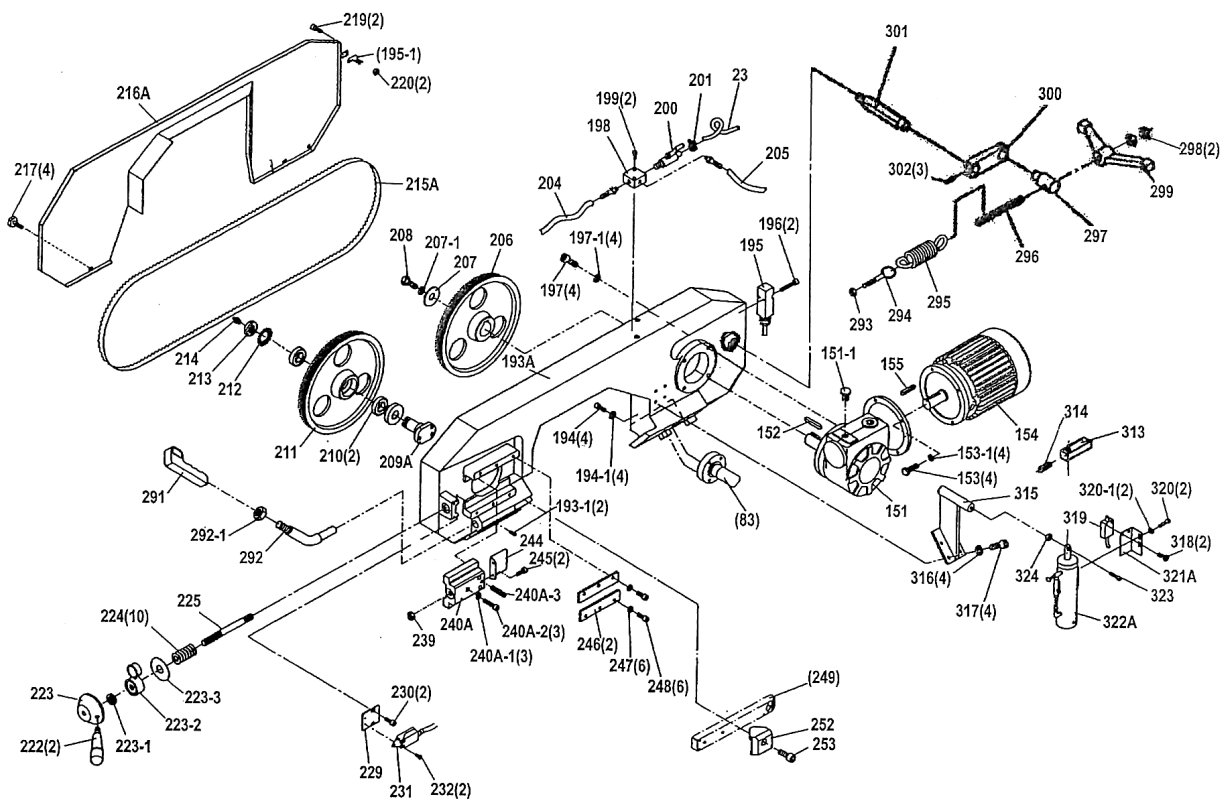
Despiece: arco de la sierra, motorreductor y volantes
